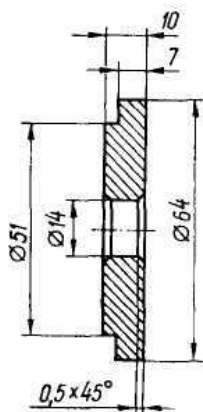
Оправка для выпрессовки наружного подшипника ведомого вала колёсного редуктора
